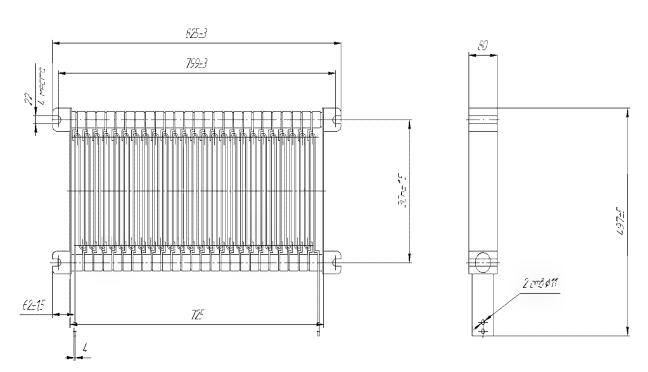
Габаритные размеры резистора типа РЛТ.
